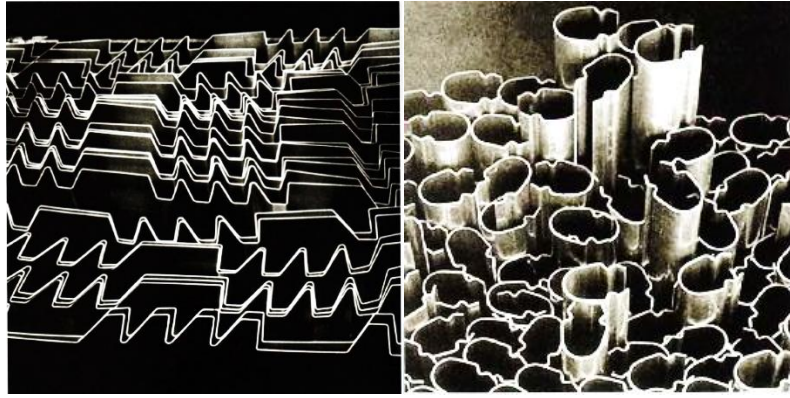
La chapa de acero plegada por Jean Prouvé
